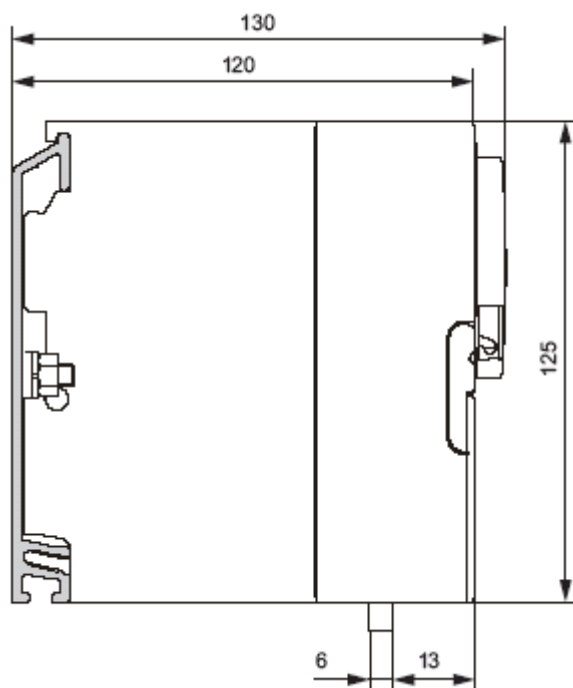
Габаритный чертеж блока питания PS 307; 5 А с CPU 313/314/315/315-2 DP, вид сбоку
